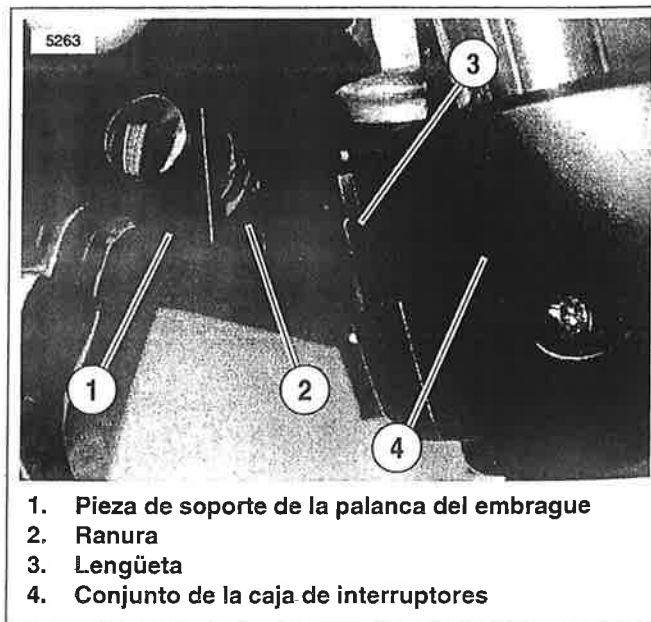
Ajuste de la pieza de soporte de la palanca de embrague en las cajas de interruptores del manillar izquierdo
